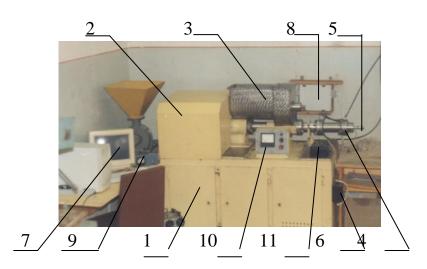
Общий вид пресс-экструдера с измерительной аппаратурой: 1 — станина; 2 — редуктор; 3 — загрузочная воронка; 4 — цилиндрический корпус шнека; 5 — формующая головка; 6 — пульт управления; 7— персональная ЭВМ; 8 — аналого-цифровой преобразователь (АЦП); 9 — тахометр; 10 — амперметр; 11 — ваттметр
